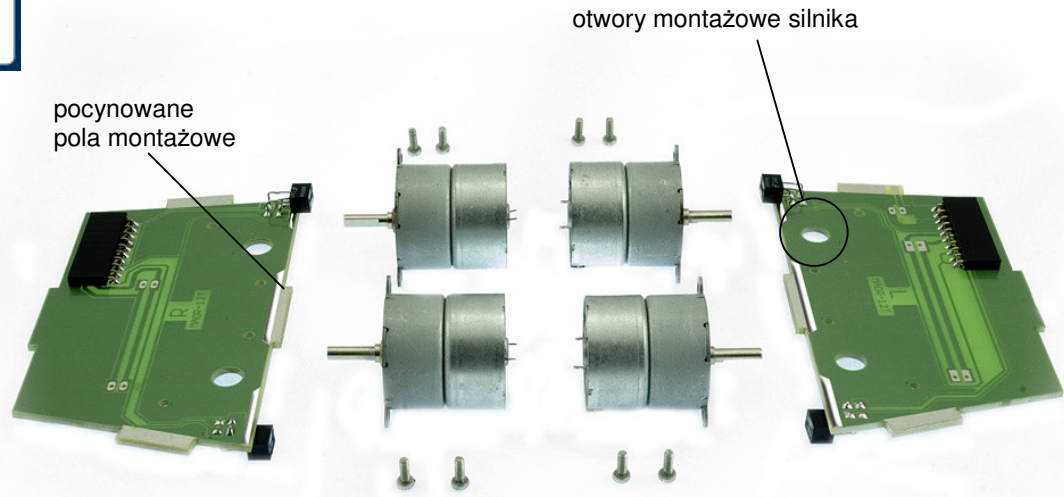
Złącza kątowe, zamontowane na płytkach od strony ścieżek
